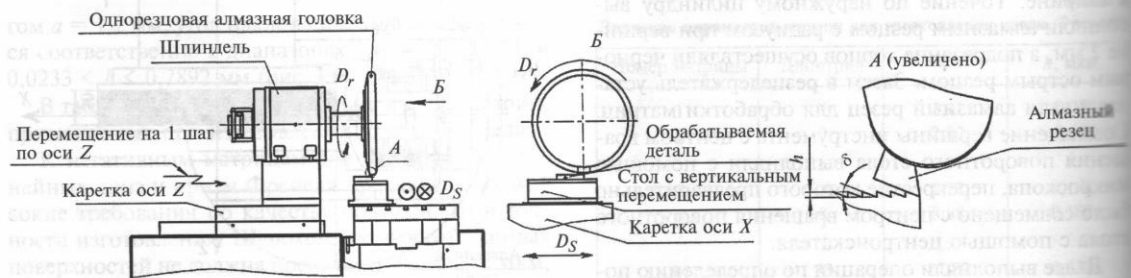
Схема обработки матриц для изготовления призм Френеля
